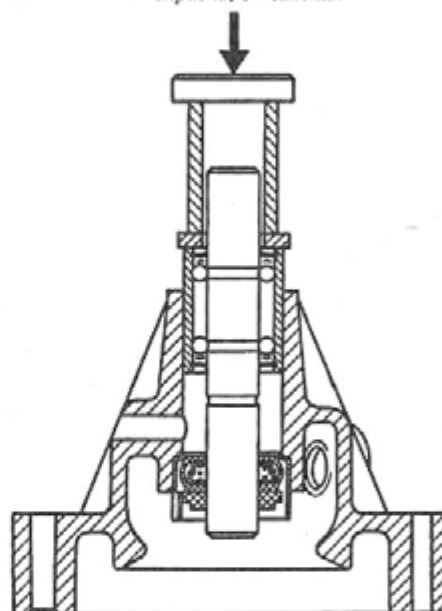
Запрессовывание подшипника с валом в корпус водяного насоса
